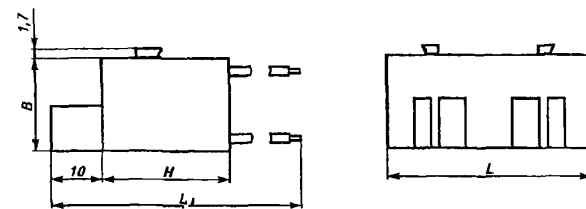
Габаритные и установочные размеры ограничителя перенапряжений типа ОПН 1
